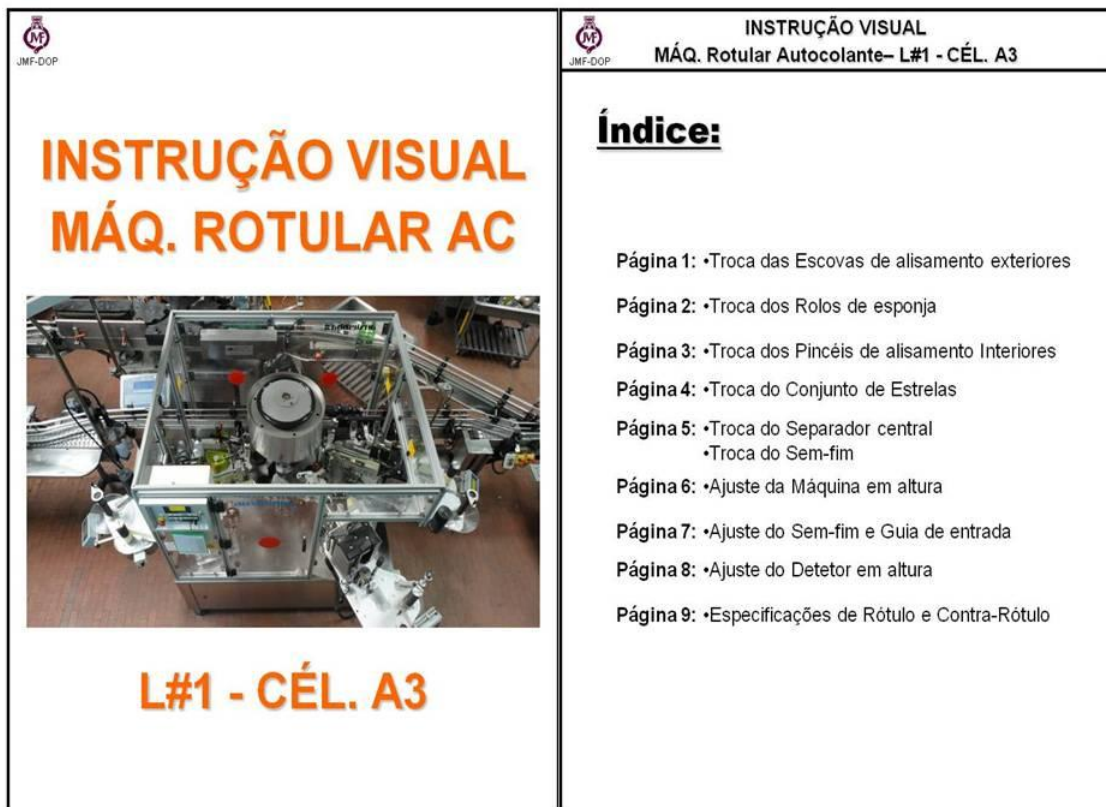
Instrução Visual Rotuladora Autocolante (Parte 1)
